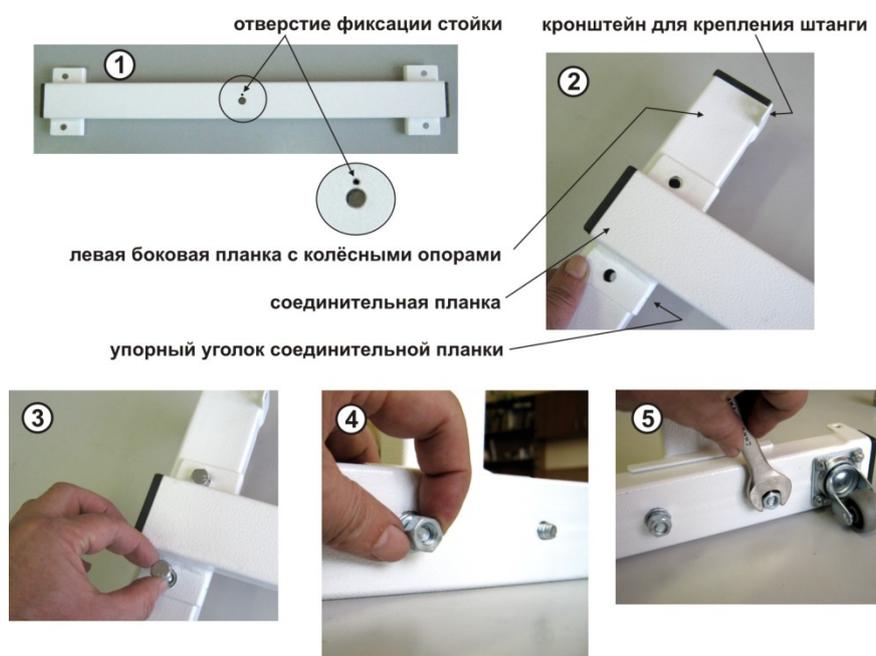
Соединение боковых планок (с колёсными опорами) с соединительной планкой основания.
